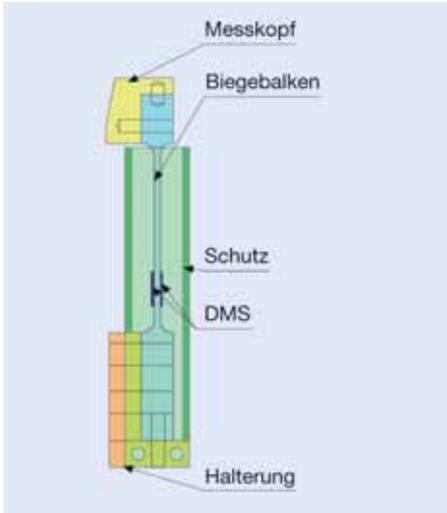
Konstruktiver Aufbau des Biegebalkens mit Applikationsvorrichtung für Gesenke.
